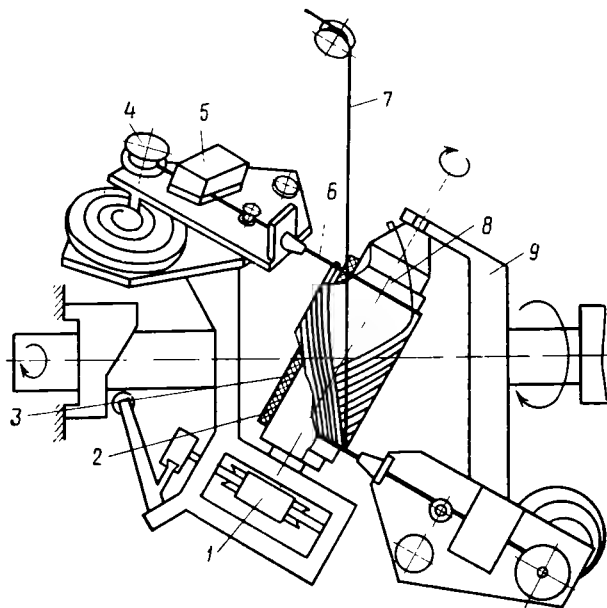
Схема намотки цилиндрической обмотки: 1 — механизм, 2 — канавки, 3 — втулка, 4 — шпуля, 5 — тормозное устройство, 6 — нити, 7 — провод, 8 — оправка, 9 — кронштейн
